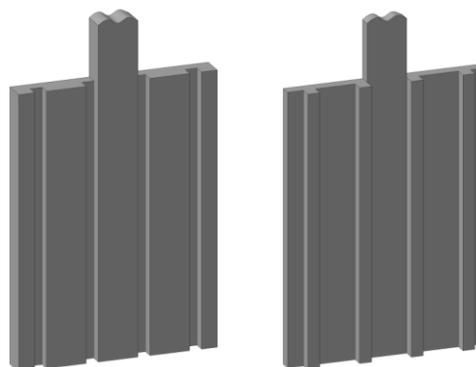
Конструкции анодов с вертикальными пазами (а) и выступами (б)
